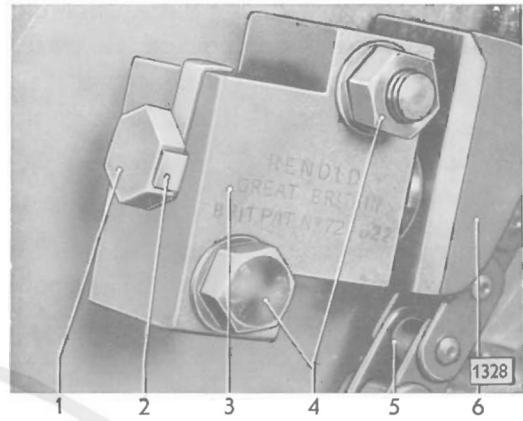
Einstellschraube mit Zungensicherung gesichert
